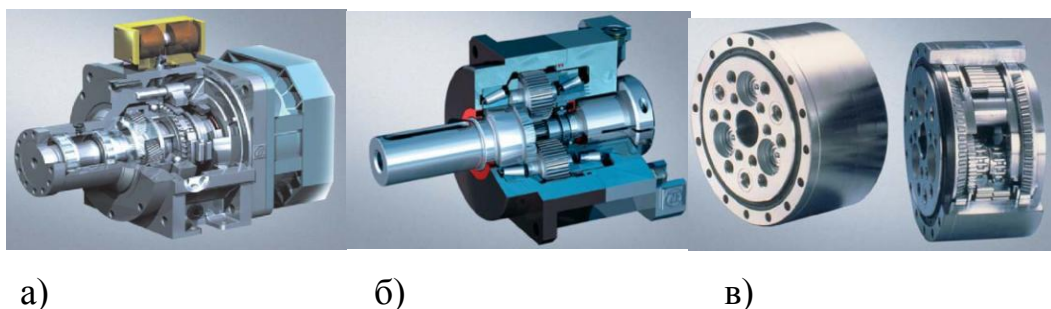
Редуктори, використовувані в верстатах з ЧПУ: а, б-планетарні;
